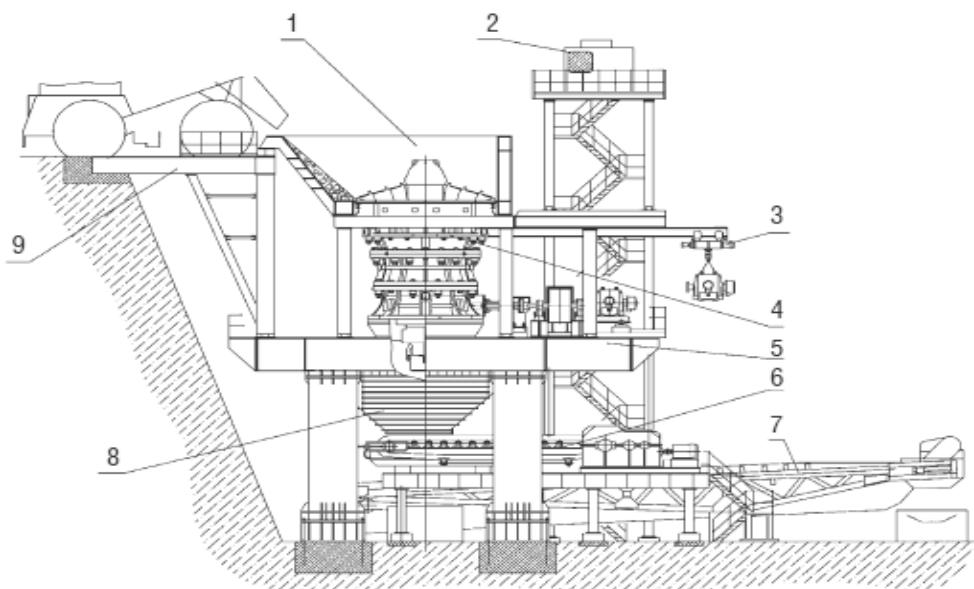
Дробильно-перегрузочная установка ДПУ-2000: 1 – приемный бункер; 2 – кабина управления; 3 – вспомогательное оборудование; 4 – дробилка ККД-1500/180; 5 – опорная рама; 6 – пластинчатый питатель; 7 – передаточный конвейер; 8 – разгрузочный бункер; 9 – эстакада
